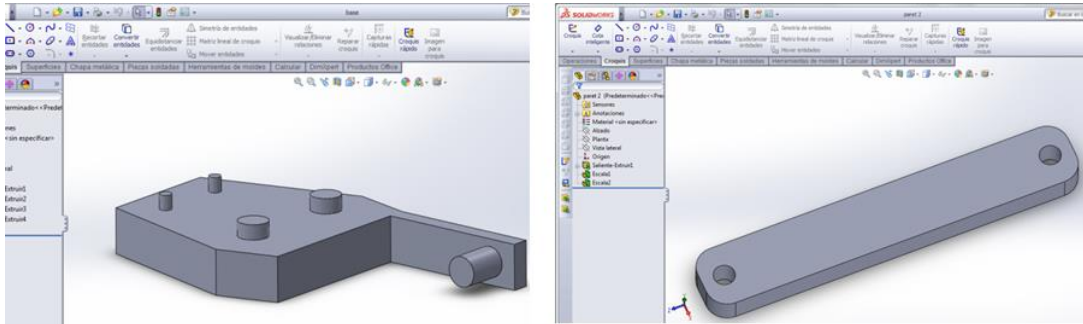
Izquierda: Base de muñeca (Pieza 8), Derecha: Pieza uno para pinza (Pieza 9).
